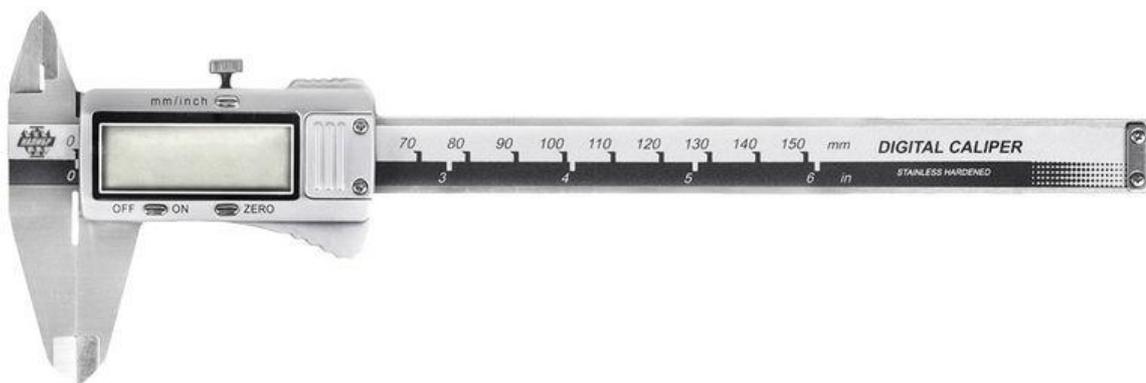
Общий вид штангенциркулей типа ШЦ-I
